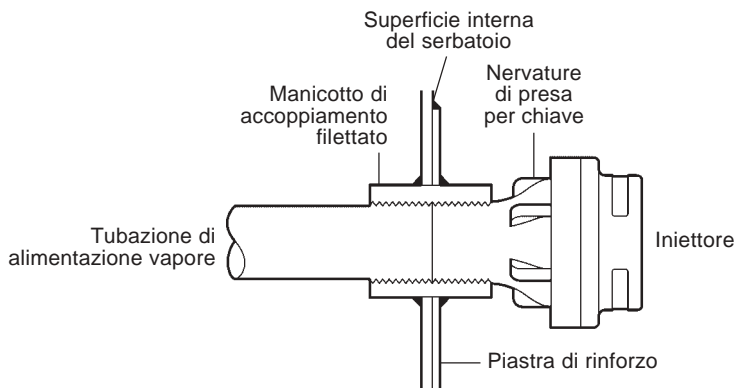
Iniettori IN25M e IN40M filettati - Tipica installazione con montaggio su bocchello saldato alla parete del serbatoio
